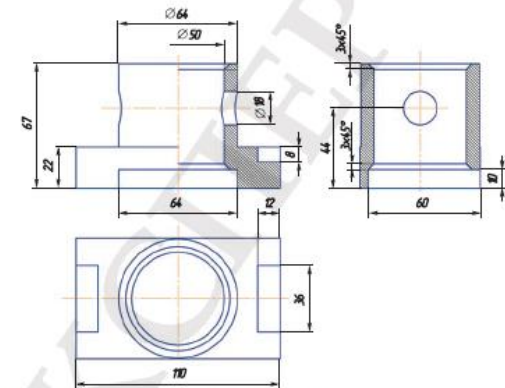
Патрубок.cdw. Чертеж с разрезами
